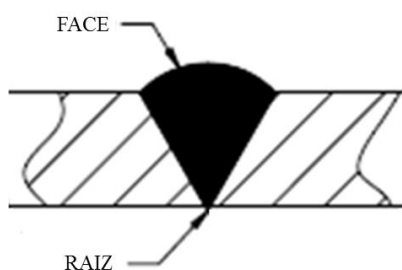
Dobramento de face e raiz do CP soldado.
